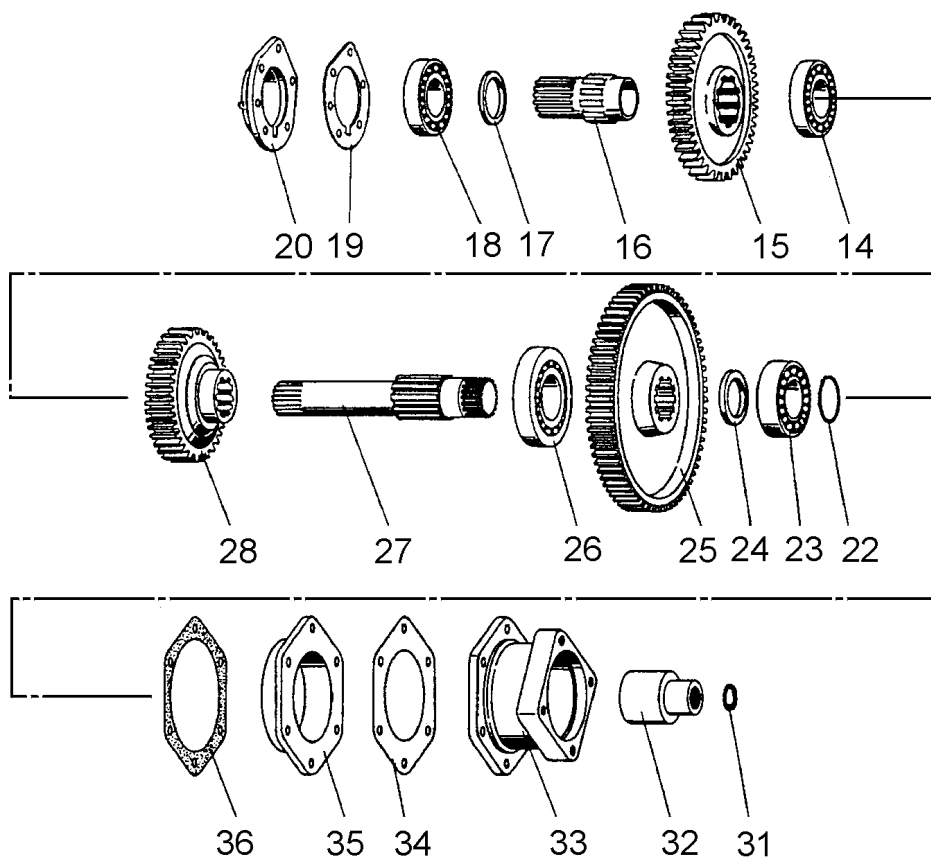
С.19. Вал быстрого (транспортного) диапазона коробки передач
